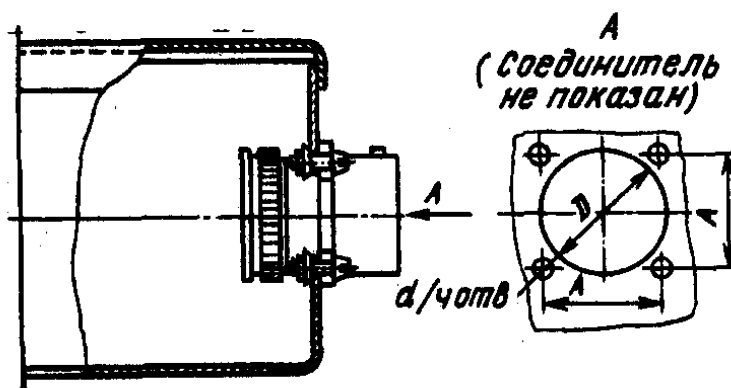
Установка и крепление соединителей СНЦ-23 в кронштейнах
